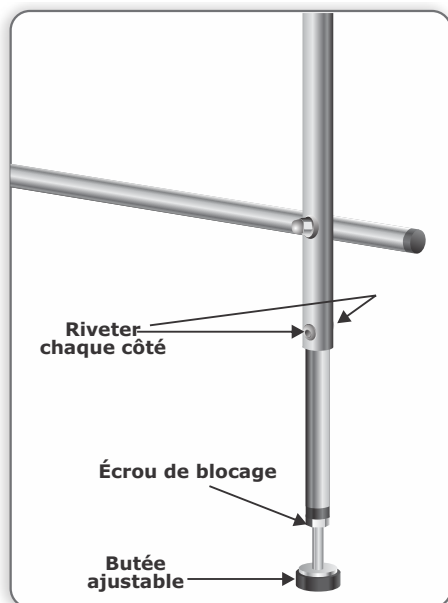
COUPER LA CLÔTURE AU CARRÉ
